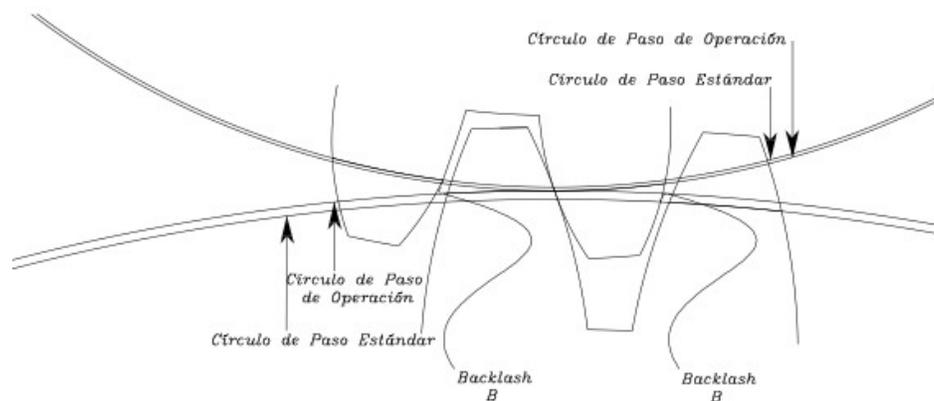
Apariencia de juego entre dientes de engranaje. Tomado de «Backlash: Juego entre dientes de engranaje» (11 p. 3)
